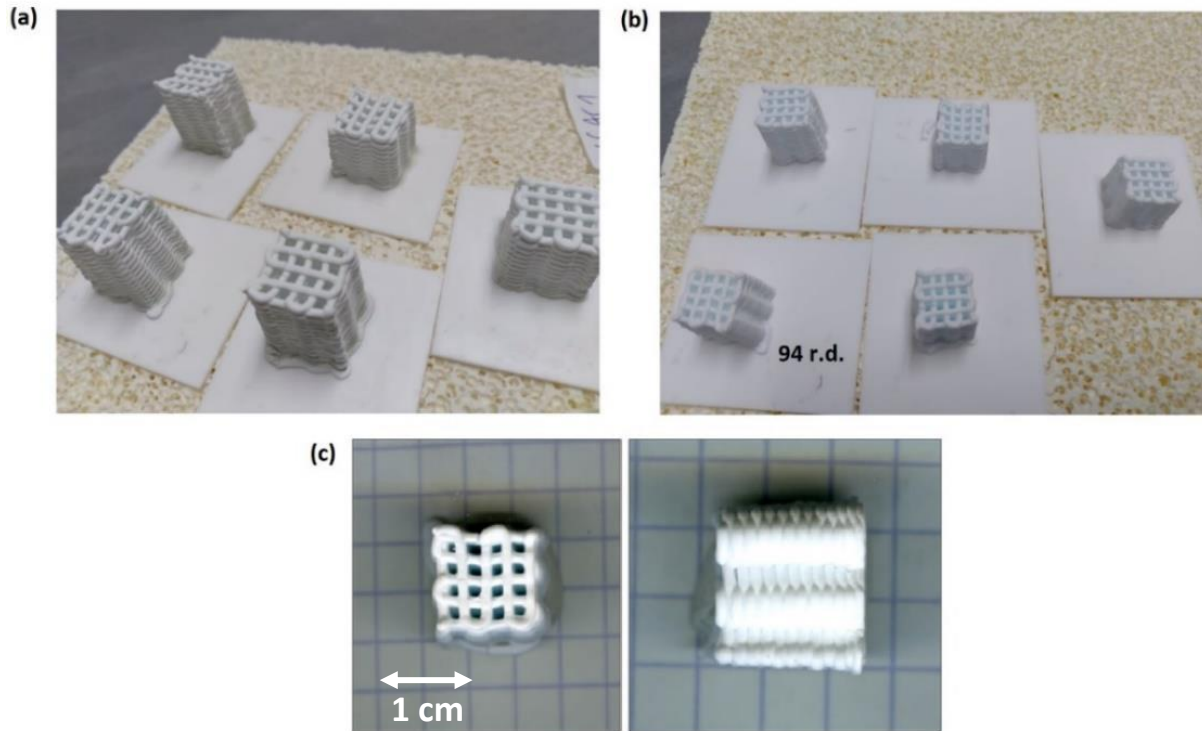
Photographies après séchage (PEG, 12h) et après frittage (1100°C , 3h) de pièces imprimées à partir de la pâte Mg-Sr-Ag-Cu 42%. (a) et (b) plusieurs pièces de type grille et (c) zoom sur une grille.
